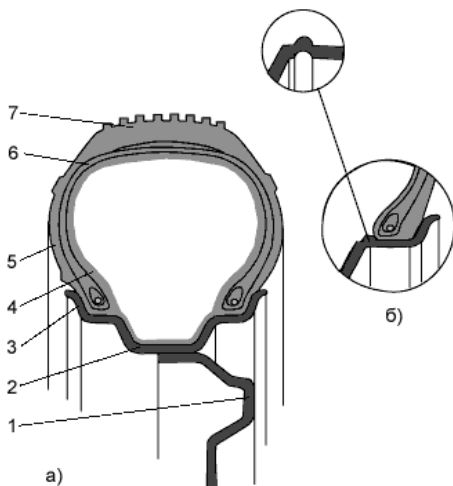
Колесо легкового автомобиля а) устройство колеса б) уплотняющий буртик на ободе бескамерной шины 1 - диск колеса; 2 - обод; 3 - борт; 4 - камера; 5 - боковина; 6 - корд; 7 - протектор
